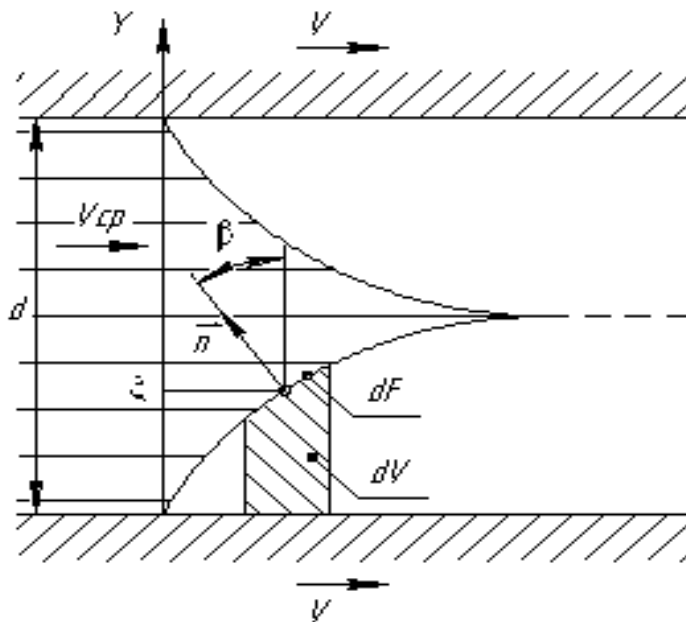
Схема затвердевания расплава при двухвалковой быстрой закалке расплава
